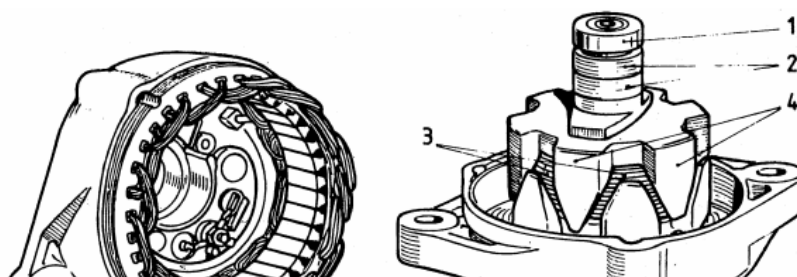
Conjunto do rotor desmontado do alternador ([6]).
